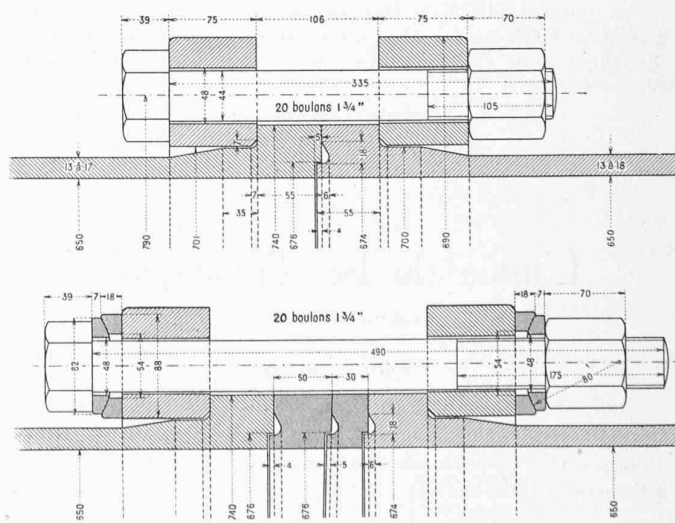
Joint à brides, système Thyssen. — 1 : 6.
